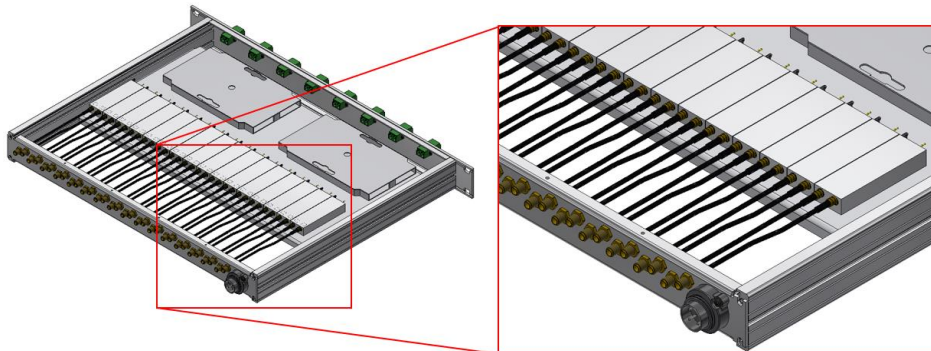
Connessione cavi coassiali e fissaggio mounting plate
